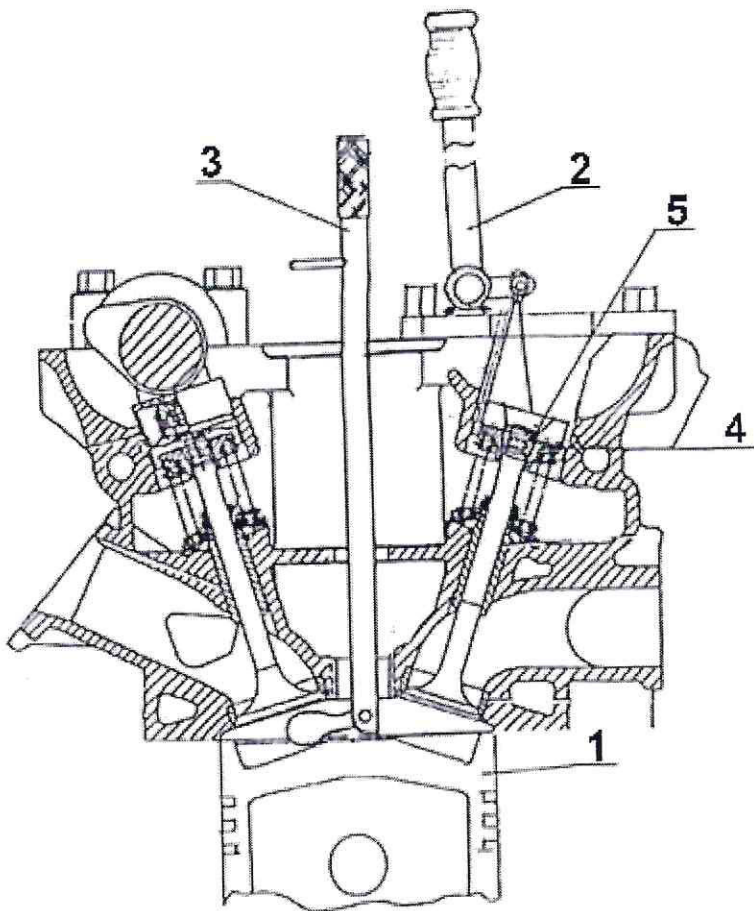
Общий вид приспособления для рассухаривания клапанов
